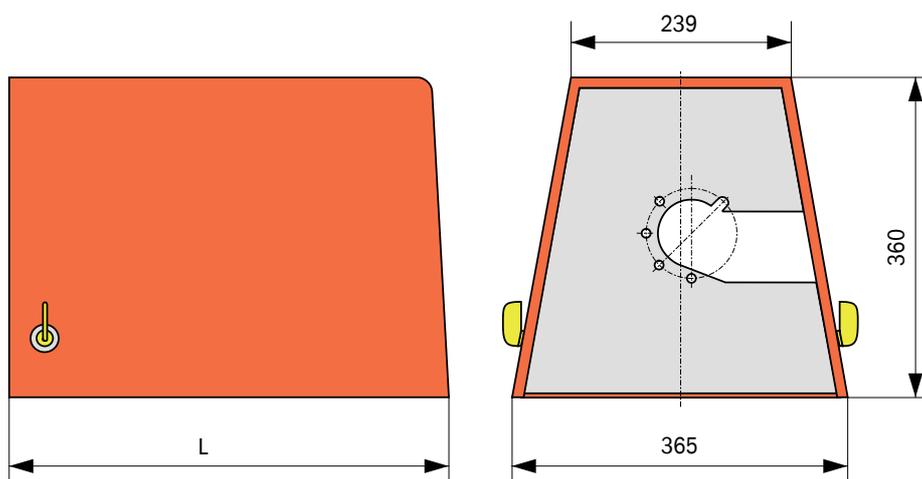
Cubierta de protección contra la intemperie para la unidad de aire de purga externa
